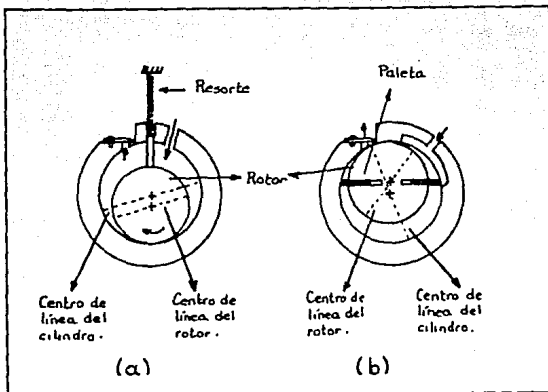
a) Compresor rotatorio de tipo pistón rodante.
